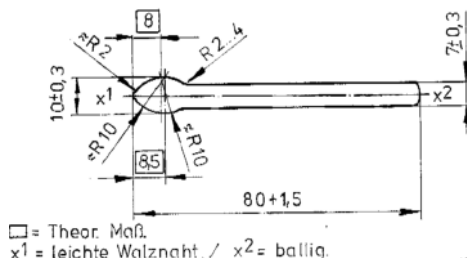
Beispiel für ein strömungsgünstiges Rechenstabprofil (hier: 80 x 10/7 mm; Walzwerke Einsal GmbH Profilnr.:1/08380/0)
